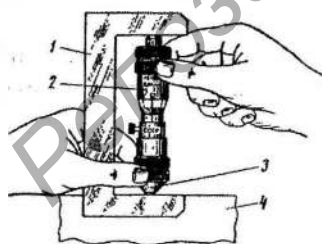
Проверка нулевого положения микрометрического нутромера: 1 — установочная мера, 2 — микрометрическая головка, 3 — наконечник, 4 — поверочная плита [10, с. 166]
